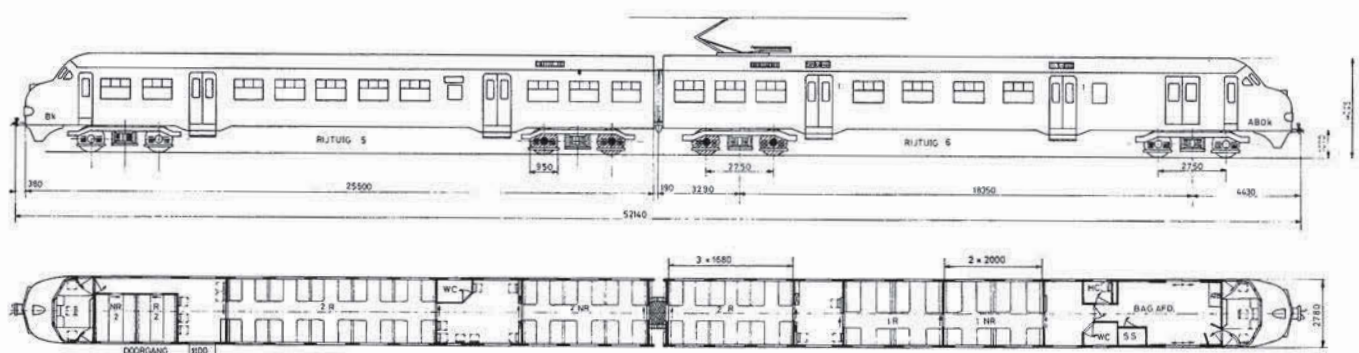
Algemeen plan treinstellen 401 - 438, levering Werkspoor
